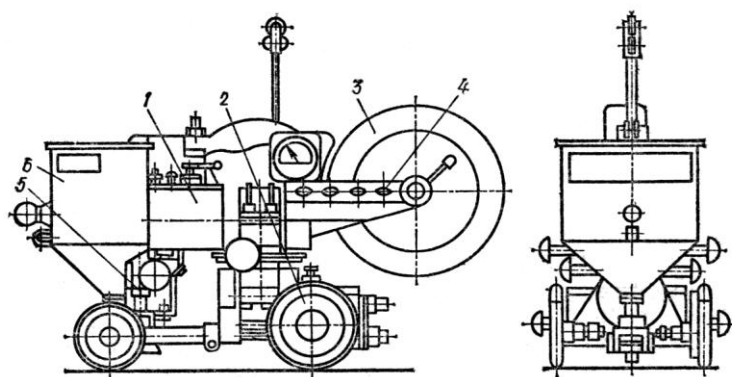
Общий вид сварочного трактора ТС-35
